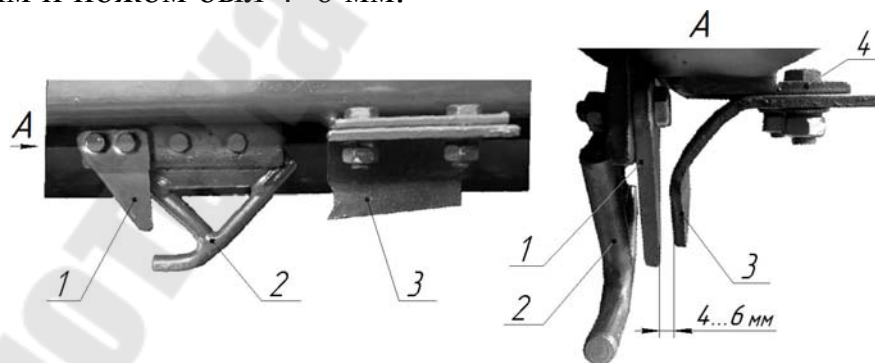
Схема регулировки положения упора: 1 – нож; 2 – поводок; 3 – упор; 4 – кронштейн
